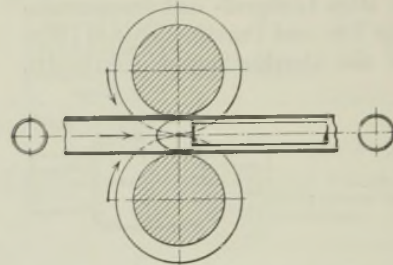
Schweißen des Rohres im Siederrohrschweißverfahren.
